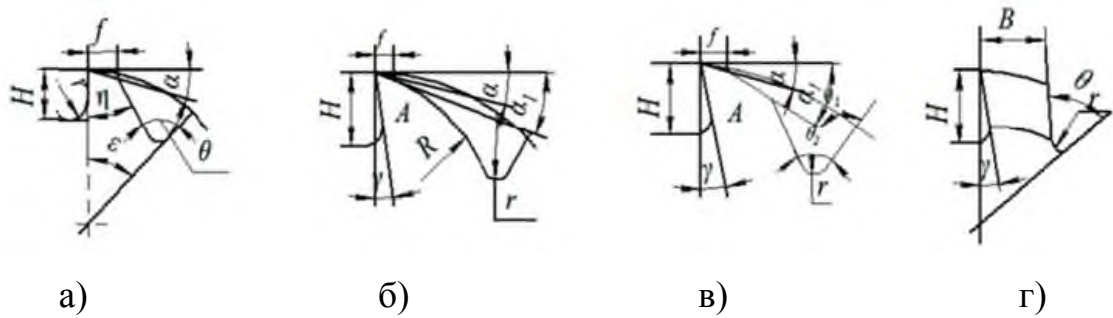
Форма зубів фрези (а - однокутова; б - параболічна; в - з ламаною спинкою; г - затилована) [34]
